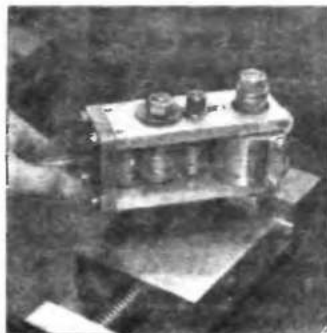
Приспособление для изгиба заготовки вкладыша
